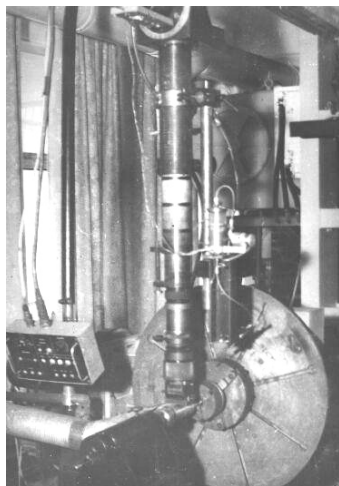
Пристрій для поверхневого лазерного пластичного деформування
